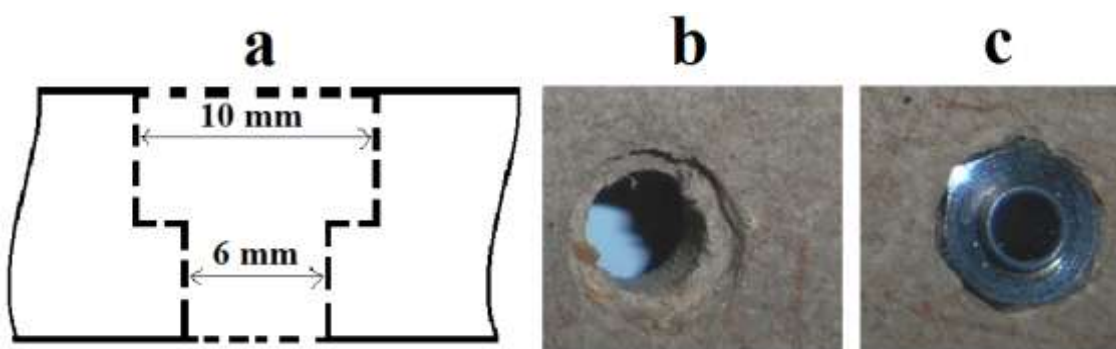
(a) Largura dos furos. (b) Foto da furação. (c) Terminal encaixado no furo.
